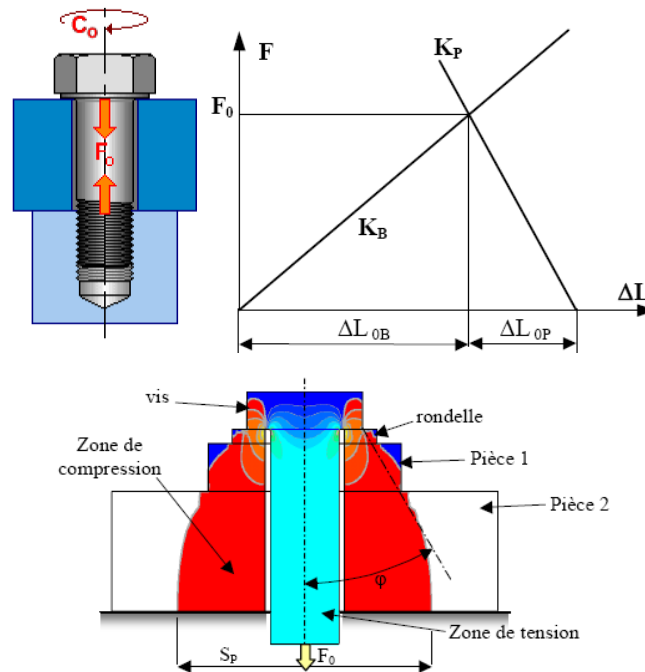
Précontrainte et couple de serrage sur un assemblage vissé.
